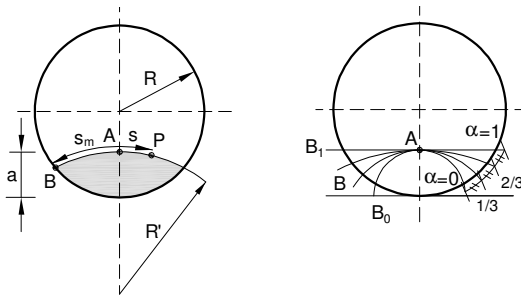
Caracterización fisuras (Levan y Royer).
